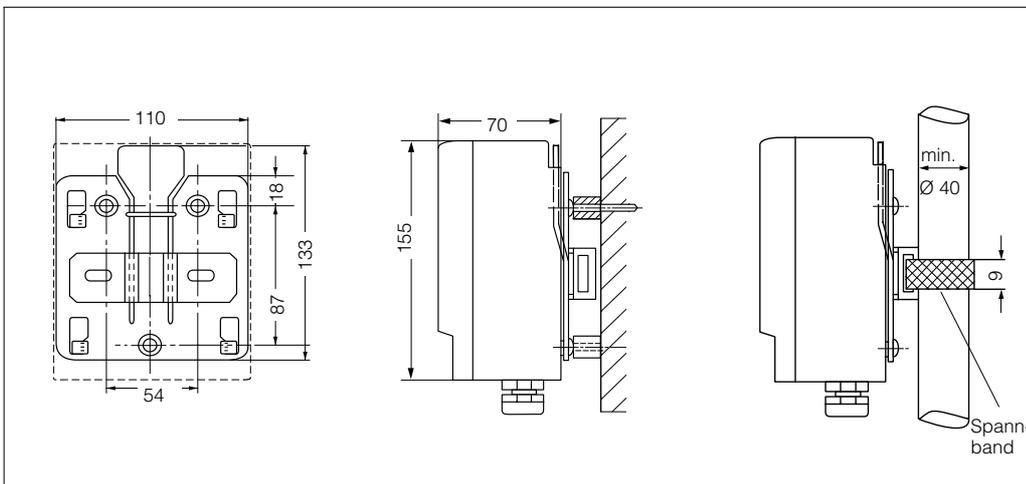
Halteplatte für Wand- und Mastmontage des separaten Meßumformers
